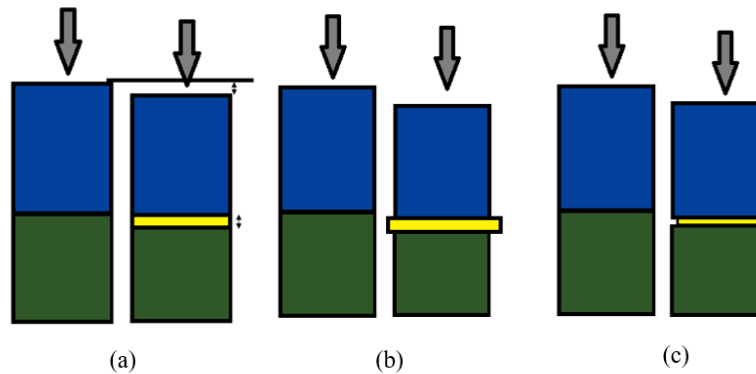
Simulação de SUS, onde demonstra a distância de soldadura((a) ideal; (b) excessiva; (c) insuficiente)
